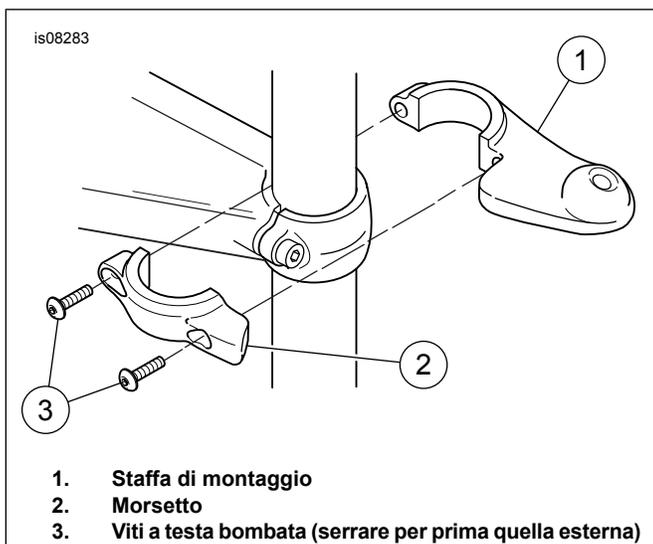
Installazione della staffa di montaggio sulla canna della forcella (illustrato il lato destro)
